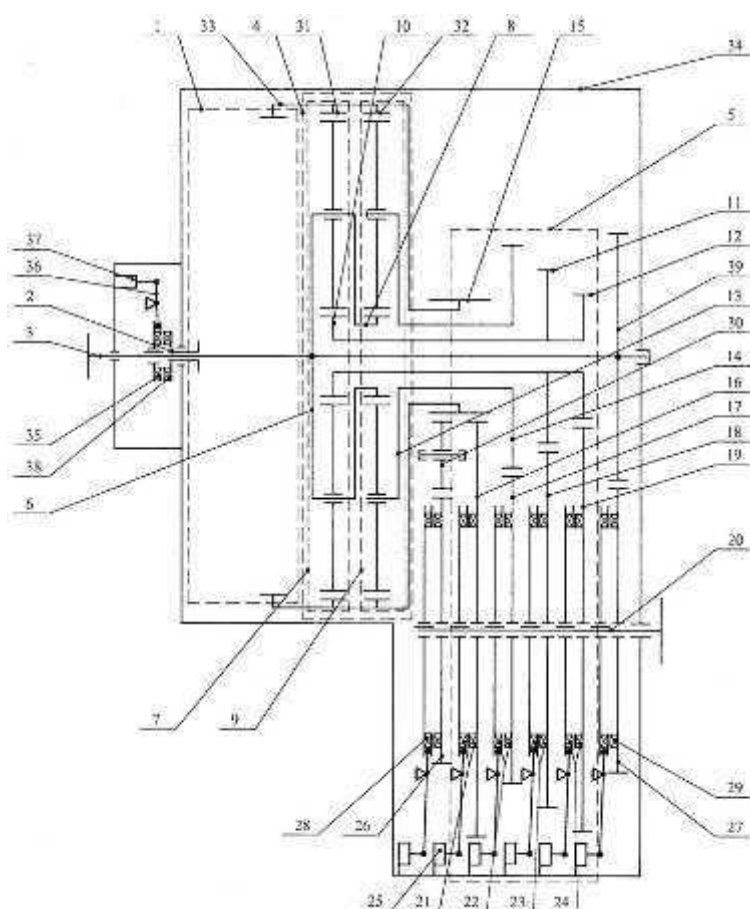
Патент РФ № 2523508 Широкодиапазонный бесступенчатый привод (супервариатор)
